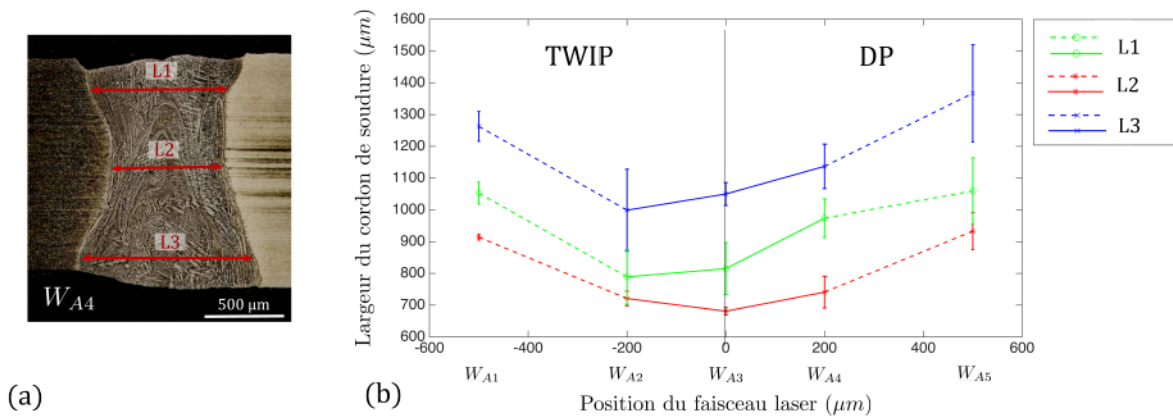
Dimensions caractéristiques d'un cordon de soudure (a) et évolution de la largeur des joints soudés fonction de la position du faisceau laser (b) (- - - « cas extrêmes »)
